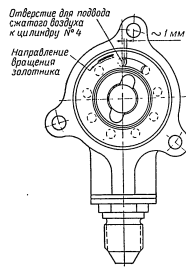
Схема установки золотника распределителя сжатого воздуха.
